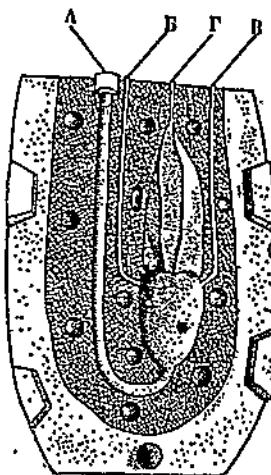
Отливка „под давлением“. Австралийский каменный нож. Задняя половина формы с гипсовым отливком и заполненными гипсом литником и воздушниками. А—литник. Б, В—боковые воздушки. Г—воздушка на остром конце отливка,
